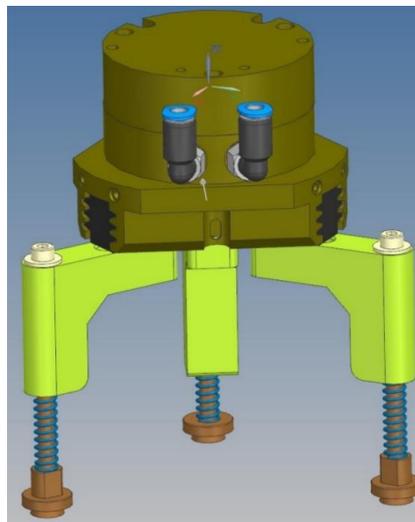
3D CAD-модель лівого захвату з пружинними пальцями
